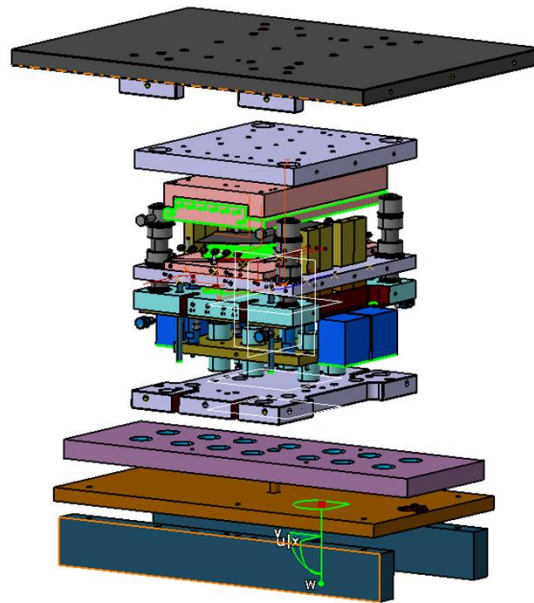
CAD Darstellung Demonstrator Bauteil Werkzeug
